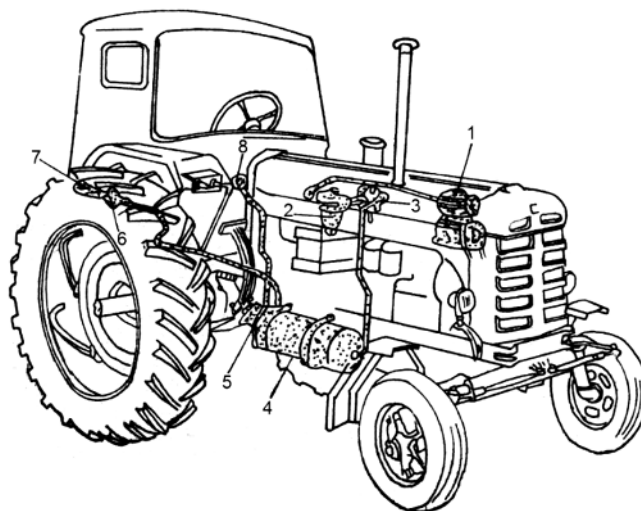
Instalația pneumatică a tractorului pentru frânarea remorcilor:
